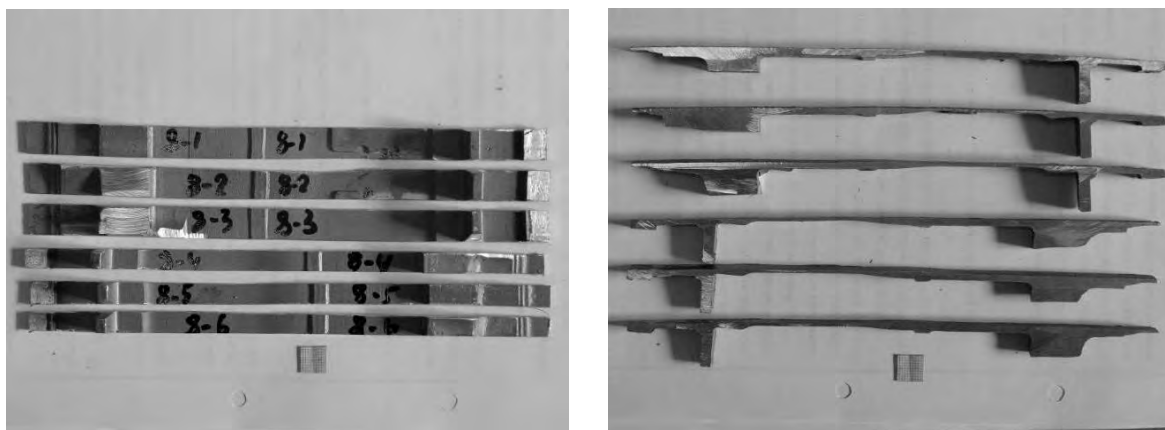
Внешний вид образцов для проведения механических испытаний с заводским сварным соединением
